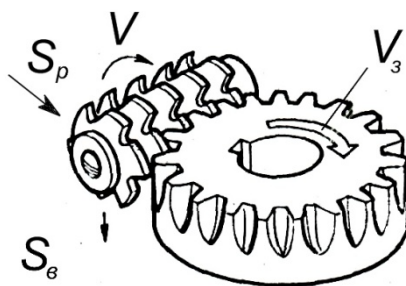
Нарезание зубьев цилиндрического колеса червячной фрезой
